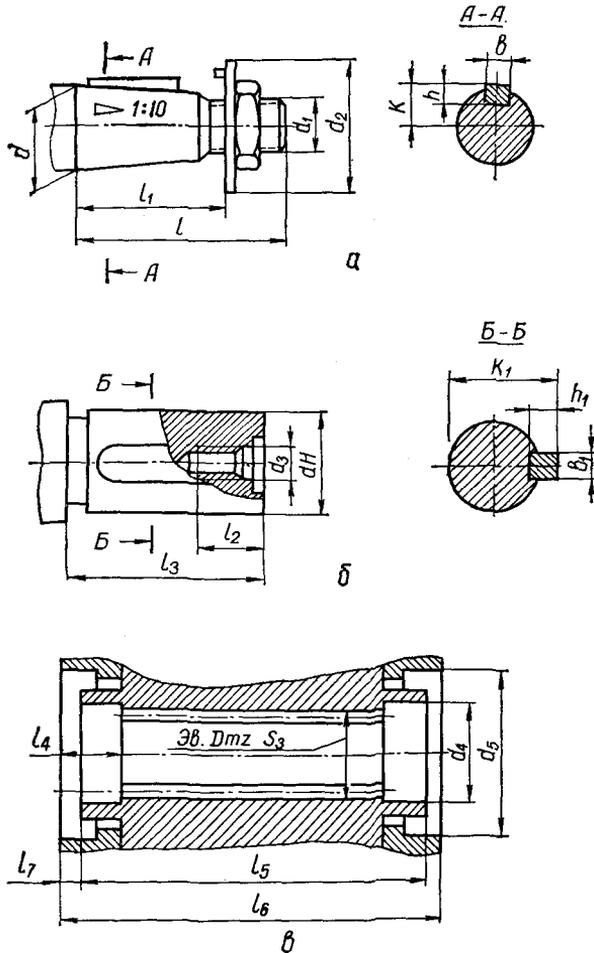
Присоединительные размеры концов валов редукторов РЧУ:
